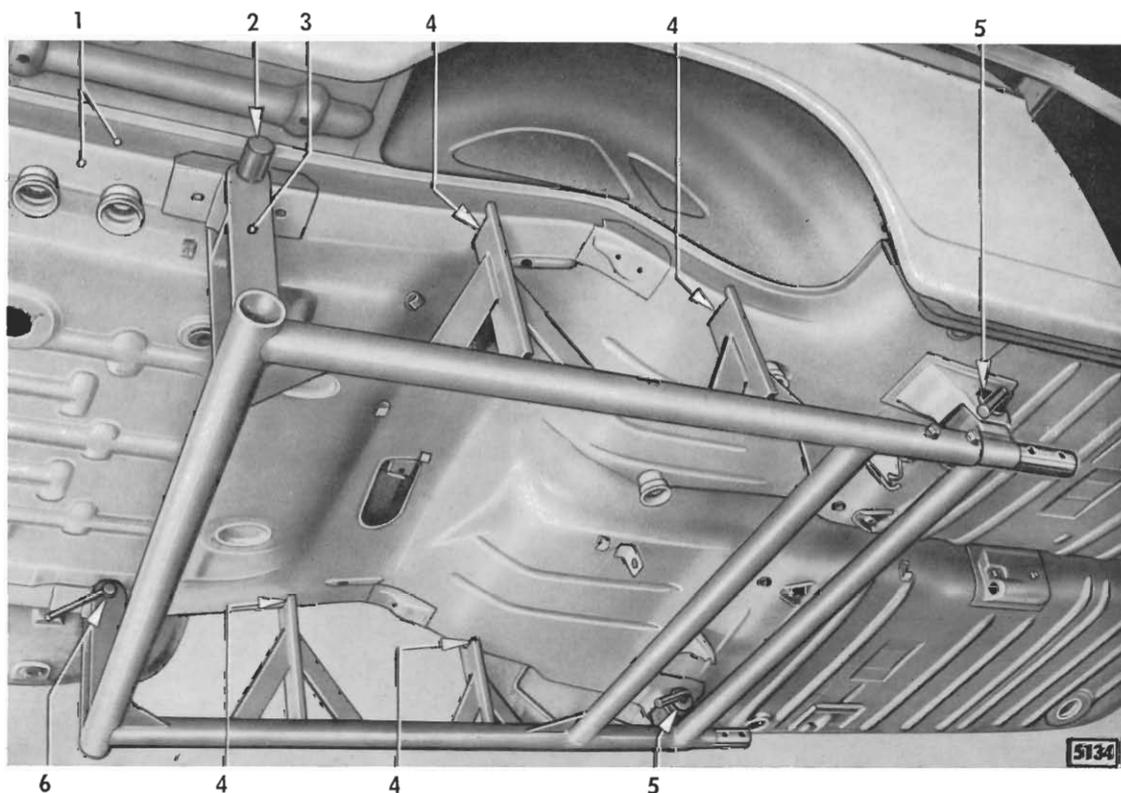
Kofferraumbodenprofil an Hinterlängsträger-Schweißlehre angepaßt
